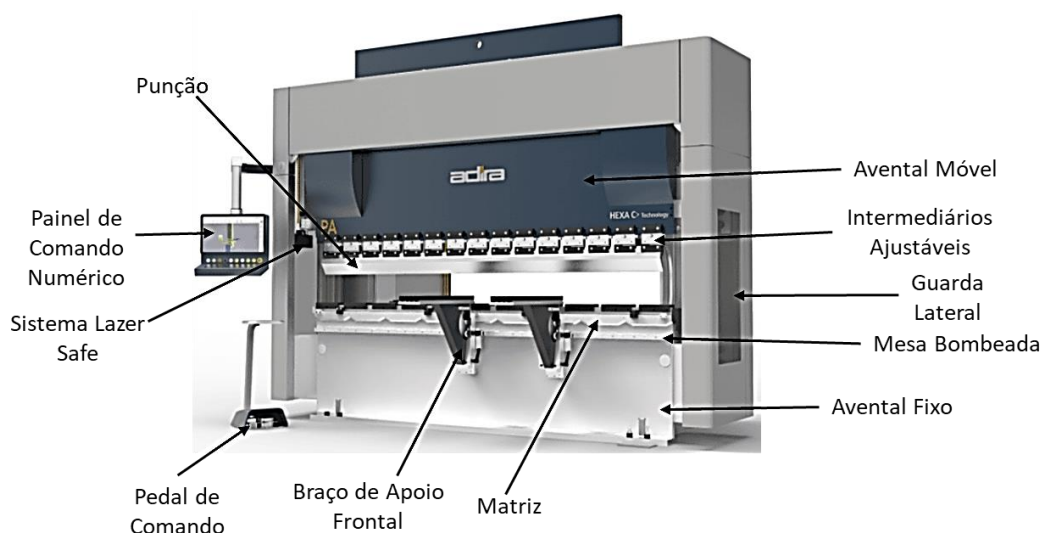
Componentes da quinadora PA através de uma vista frontal (adaptado de [2]).
